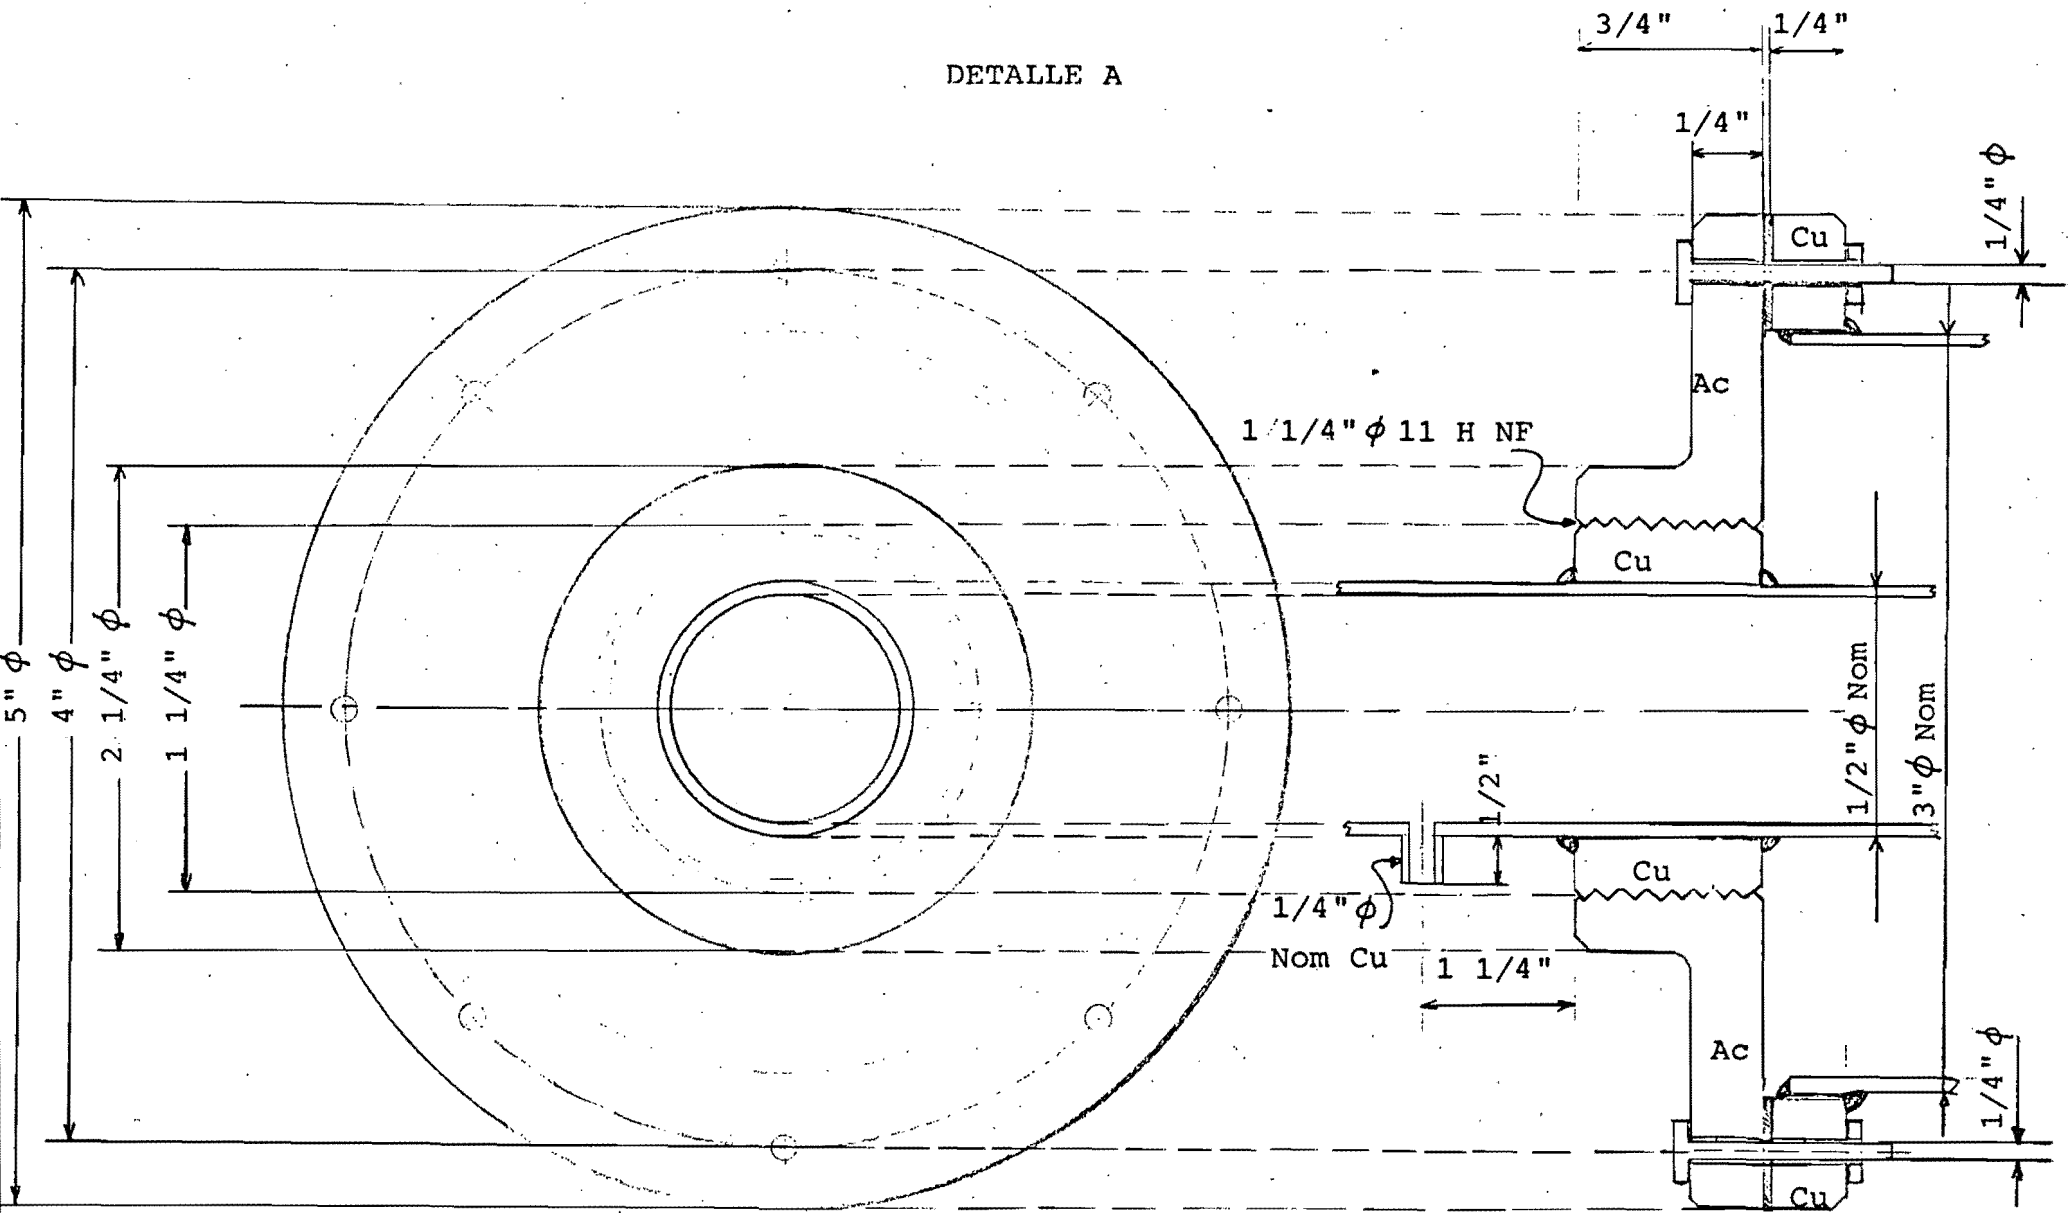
DETALLE DE CONSTRUCCION DE LA BRIDA DE MONTAJE DEL TUBO DE COBRE EXTERIOR
